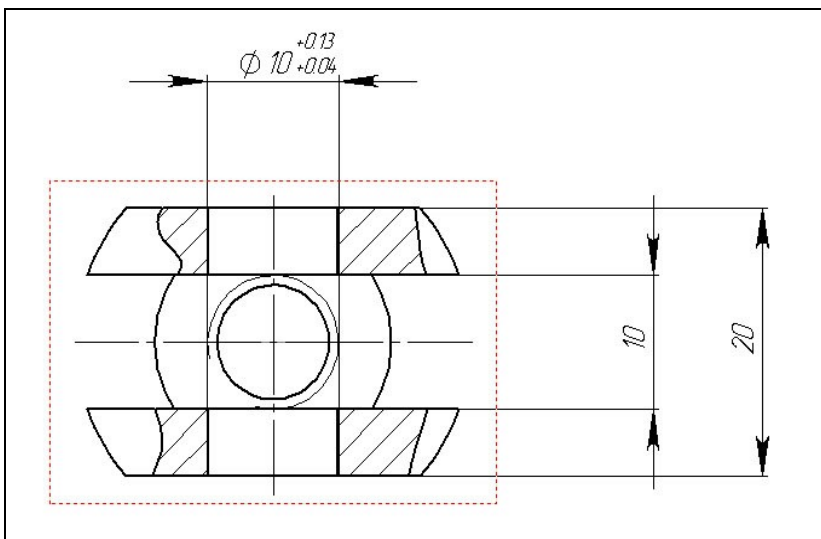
Размеры вилки для стыковки с рычагом заслонки
